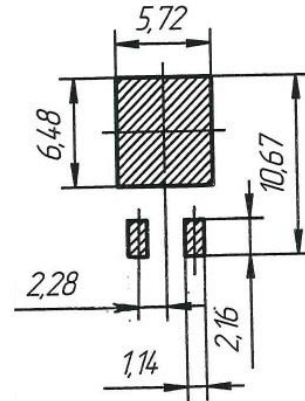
Габаритный чертеж корпуса КТ-89 (ДФЛК.430209.018ГЧ)
